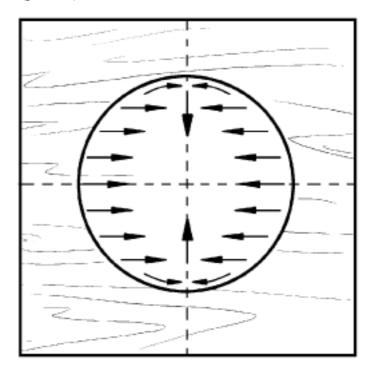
Выполнение резьбы вогнутой выемки на пласти заготовки вторым способом (стрелками показано направление движения инструмента)
